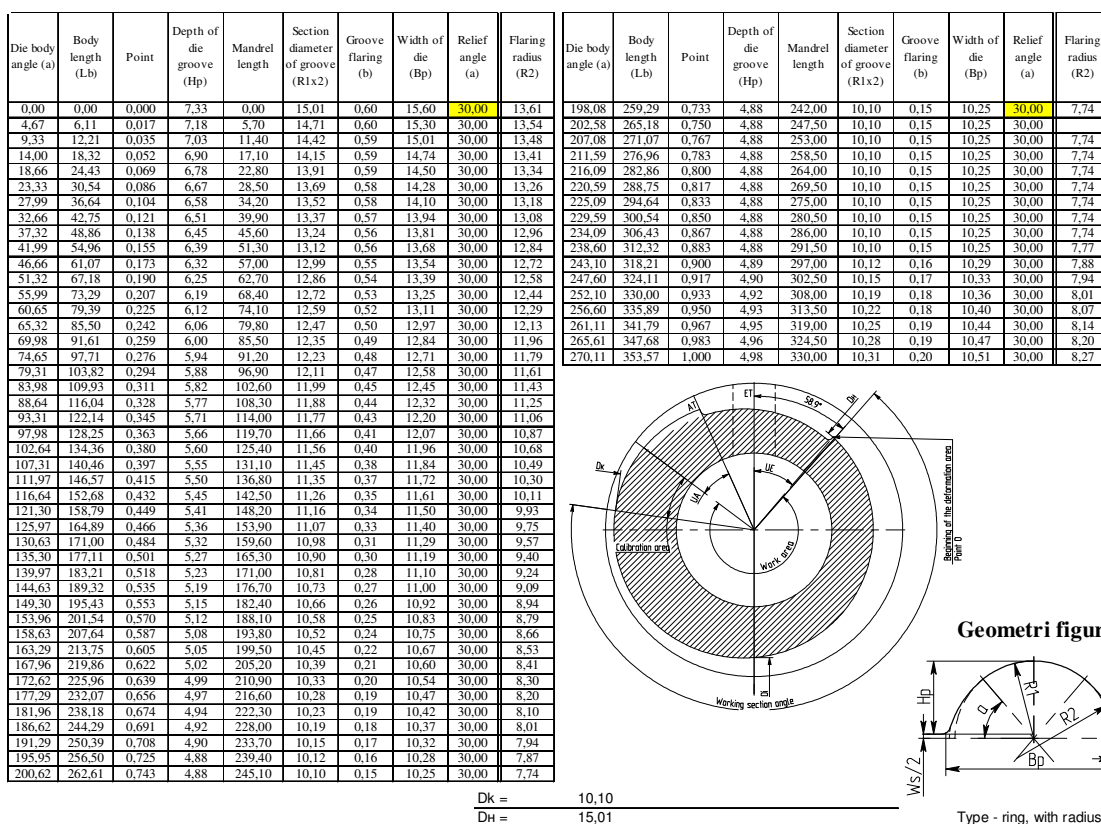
Калибровка ручья калибра, выполненная для одного из станков ЧПУ
